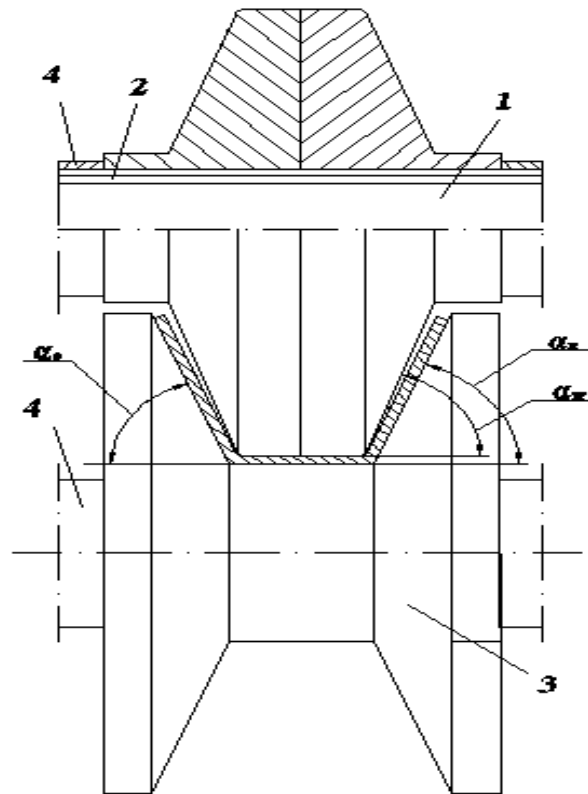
Схема валків для формування швелера: 1 - робочий вал; 2 – шпонка; 3 – профільні дискові елементи; 4 – дистанційні дискові елементи
